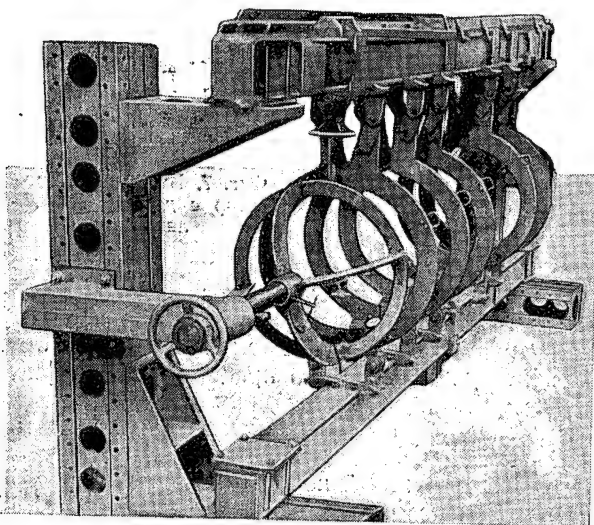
Крепление продольной балки на вертикальной колонне.
